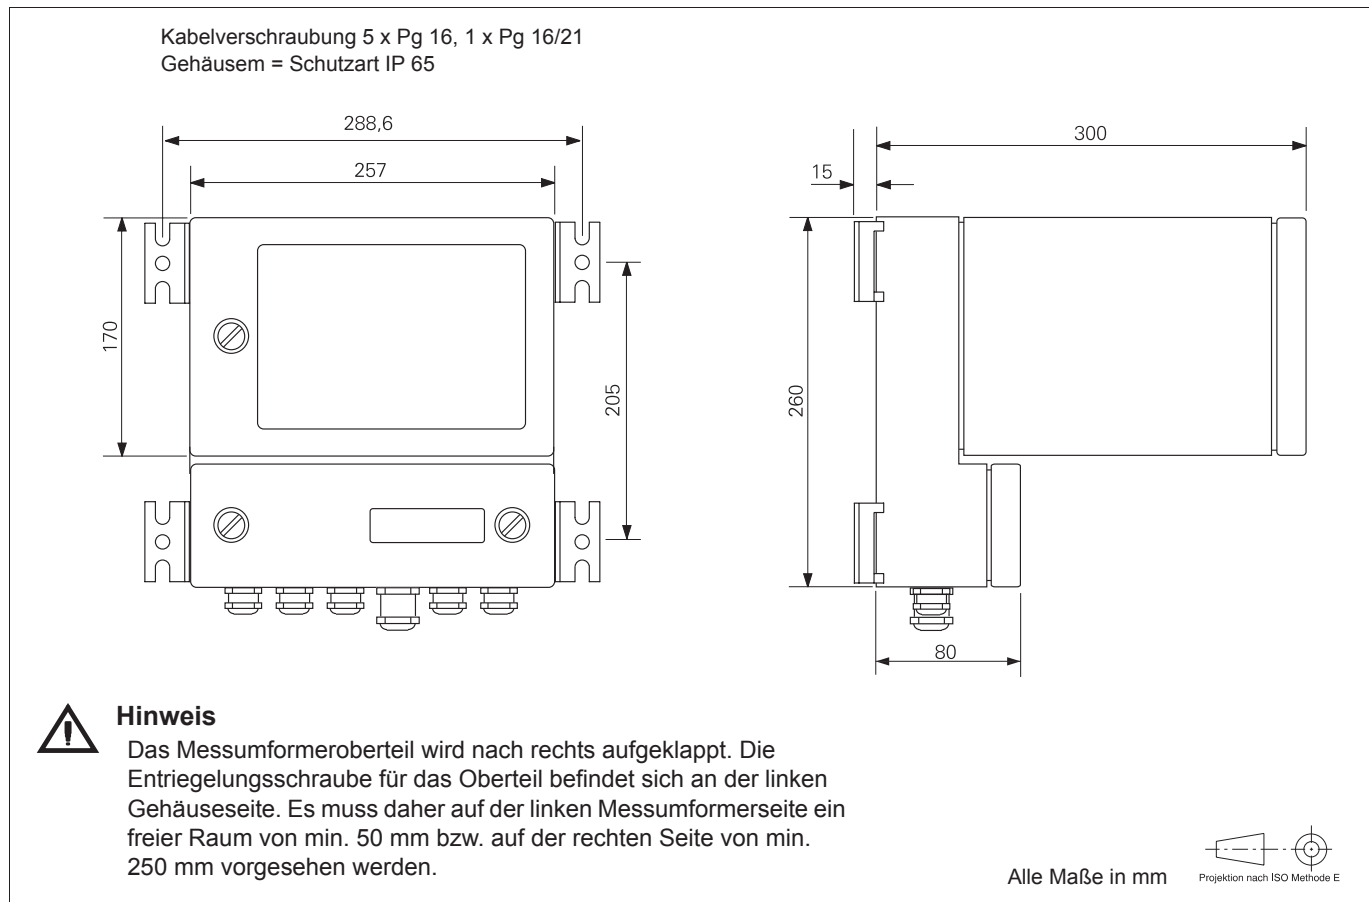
Maßzeichnung, Feldgehäuse Messumformer MAG-XP
